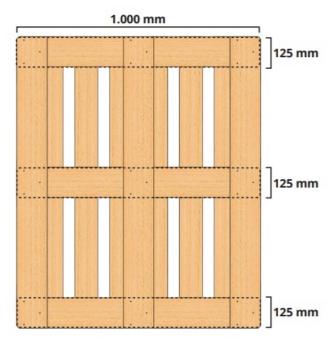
Esquema de vista inferior de um pallet com tábuas de ligação com 1200 mm de comprimento e 125 mm de largura.
